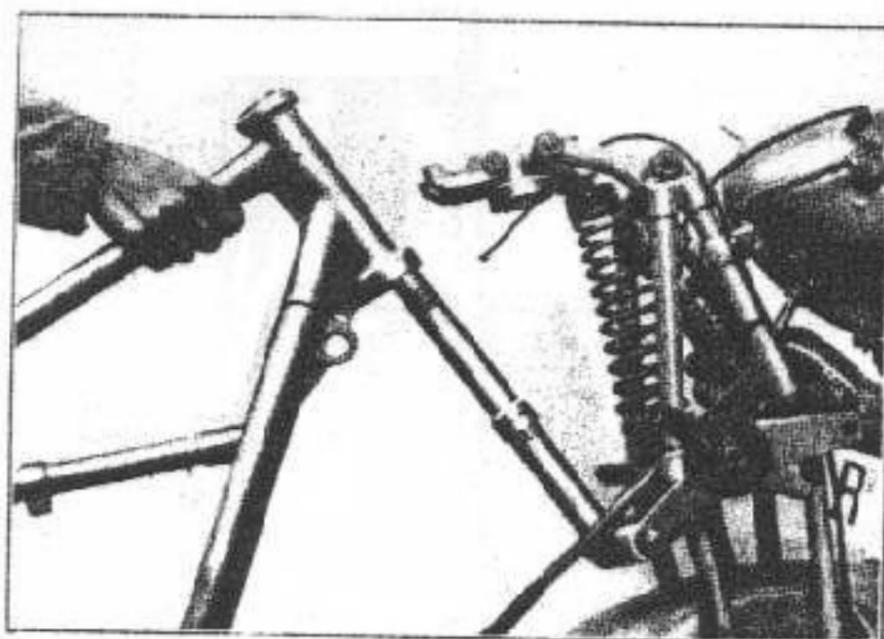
Come si sfila il canotto di guida dal canotto del telaio (pipa di sterzo).
